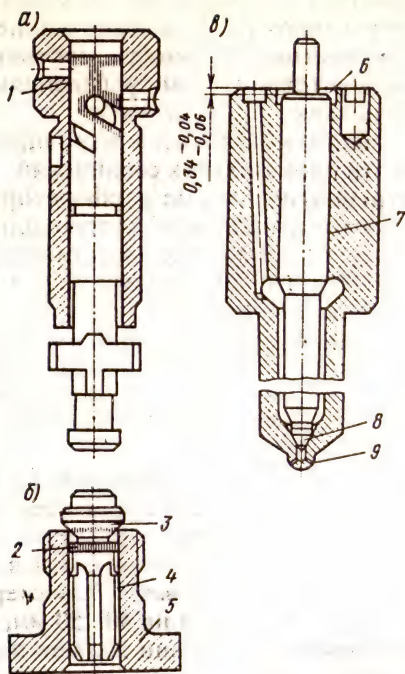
Обрабатываемые поверхности: а — плунжерной пары; б — нагнетательного клапана; в — распылителя форсунки; 1 — направляющая поверхность плунжера и втулки плунжера; 2 — разгрузочный поясок клапана; 3 — конусная поверхность клапана; 4 — направляющая поверхность клапана и седла; 5 — торец седла клапана; 6 — торцевая поверхность корпуса распылителя; 7 и 8 — соответственно направляющая и конусная поверхности иглы и корпуса; 9 — сопловые отверстия
